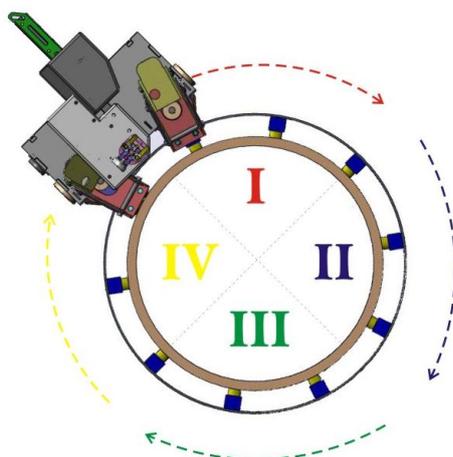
Posições de soldagem simuladas para a soldagem em dutos [5]: I - plana; II - vertical descendente; III - sobre-cabeça e IV - vertical ascendente.
